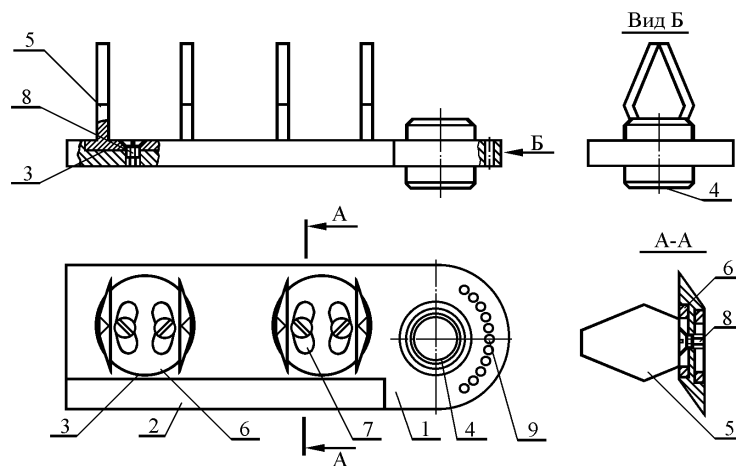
Разрушающий элемент измельчителя-смесителя кормов:
